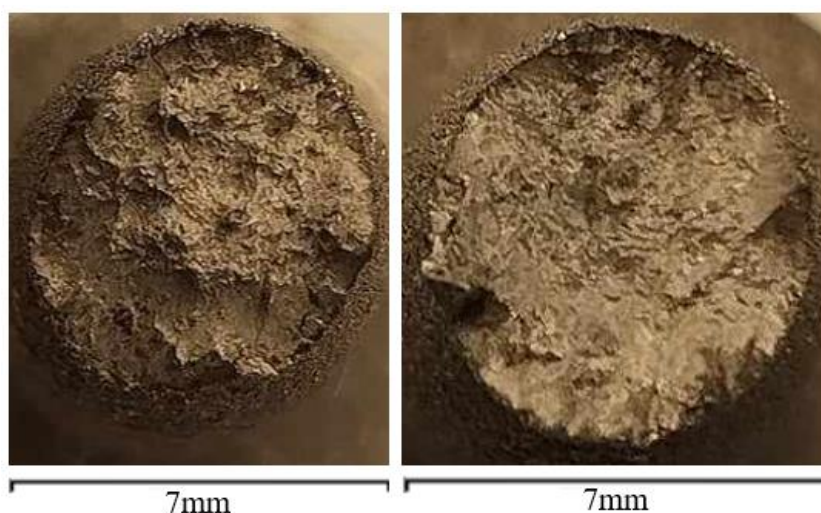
Superfície de fratura macroscópica do provete L4T3.
